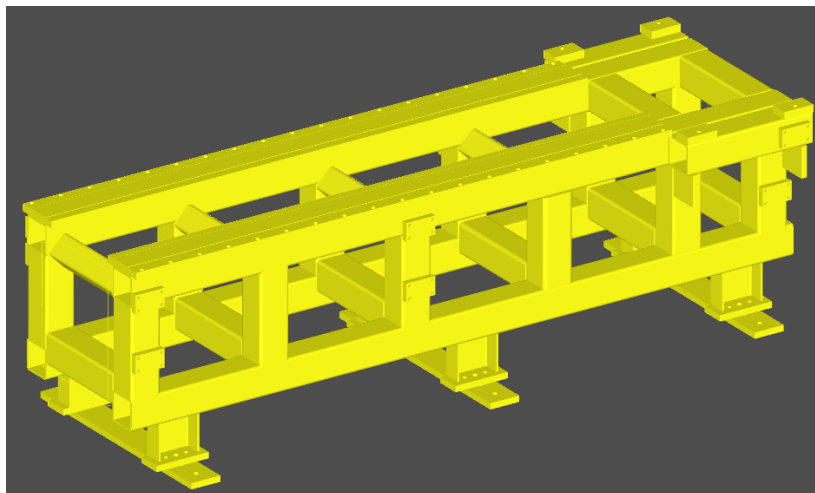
3D-CAD-Modell (Step-File) eines geschweissten Maschinenrahmens
